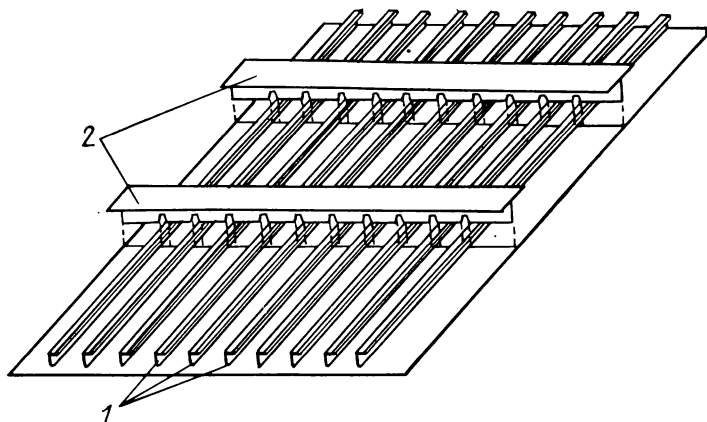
Раздельный способ сборки и сварки плоскостной секции.
